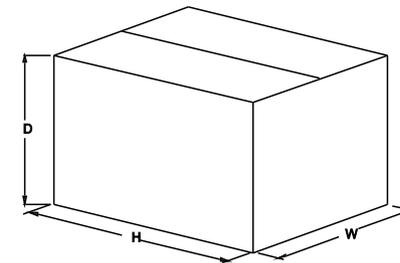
Габаритные размеры упаковочной тары
